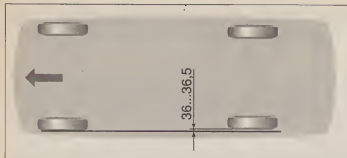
Проверка установки левого переднего колеса для движения по прямой.
